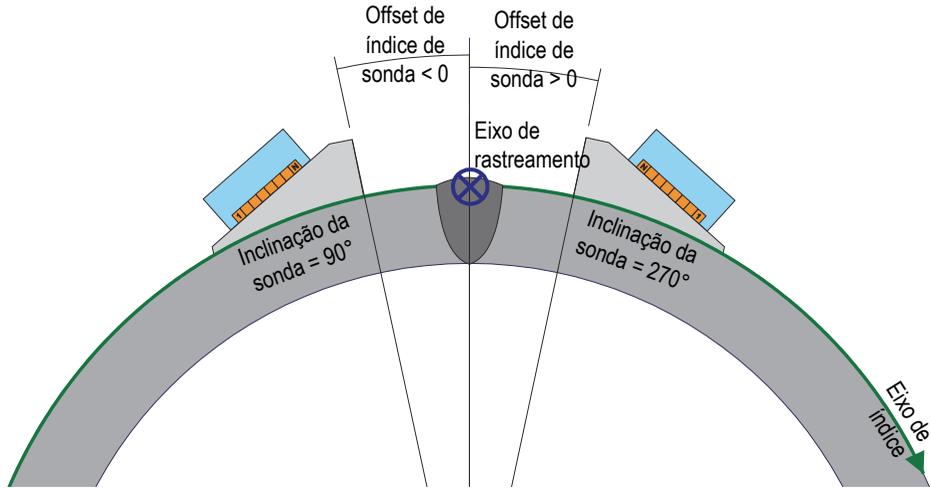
Inspeção de solda de tubos com inclinação de sonda a 90° e 270°
